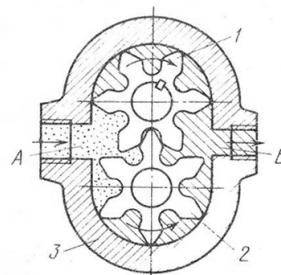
Схема шестеренного насоса: 1, 2 – шестерни; 3 – корпус
